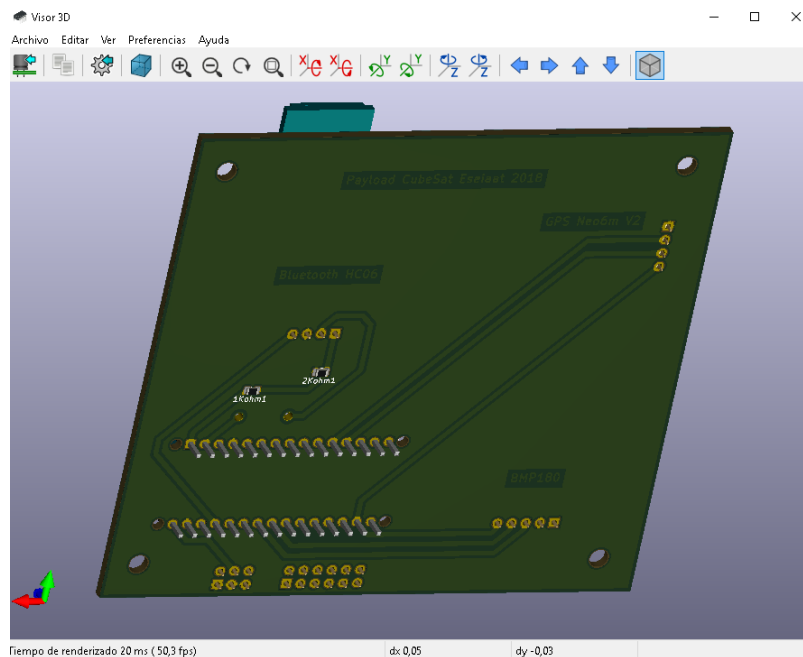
Imagen 23.- Vista inferior PCB en 3D Viewer KiCAD
